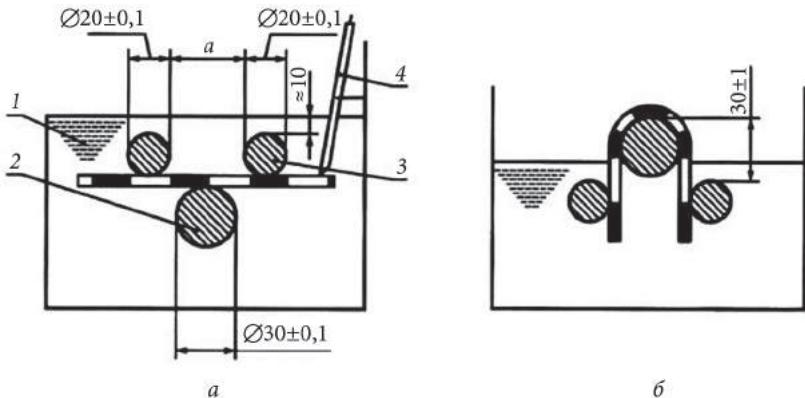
Конструкция и принцип действия изгибающего приспособления:
